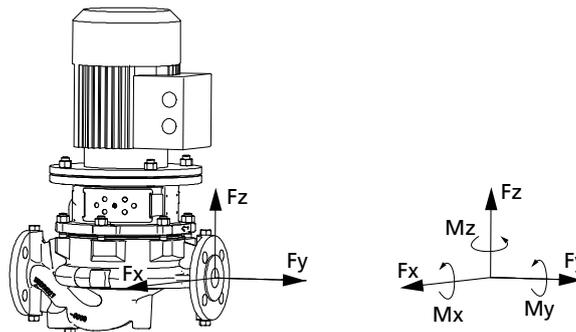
Fuerzas y pares en la tubuladura de la bomba
